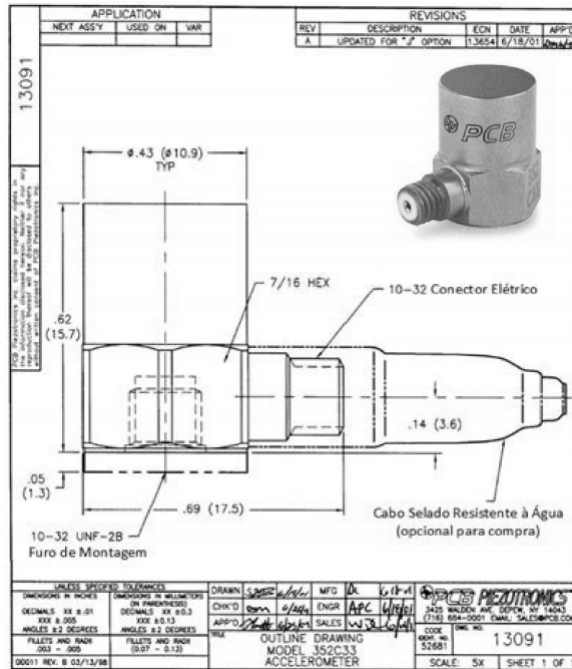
Layout de dimensional do acelerômetro PCB MOD.ICP 352C33 - Fonte original - www.pcb.com
